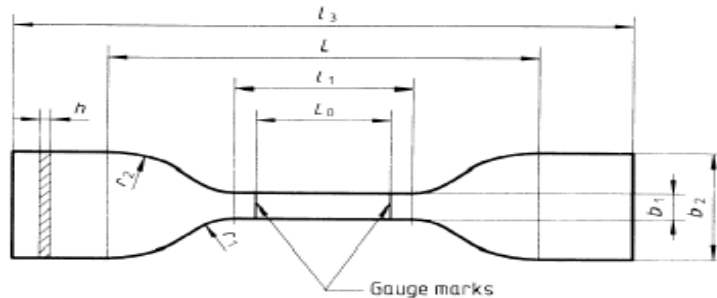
Forma y dimensiones de la probeta del ensayo de tracción
